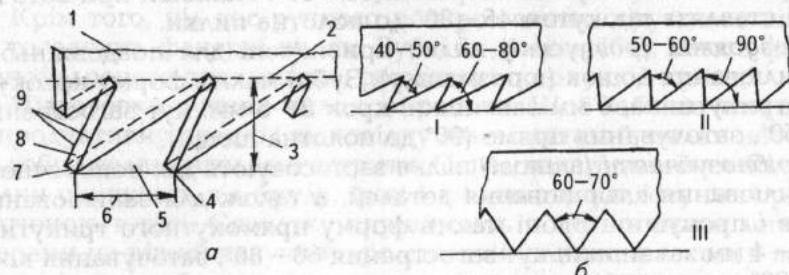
Елементи пилок і кути їх зубців: а — елементи пилки; 1 — полотно пилки; 2 — лінія основи зубців; 3 — висота зубців; 4 — вершина; 5 — пазуха; 6 — крок; 7 — передня кромка; 8 — бокові різальні кромки; 9 — бокові різальні кромки; б — кути зубців пилки для розшилювання (I — поздовжнього; II — змішаного; III — поперечного).
